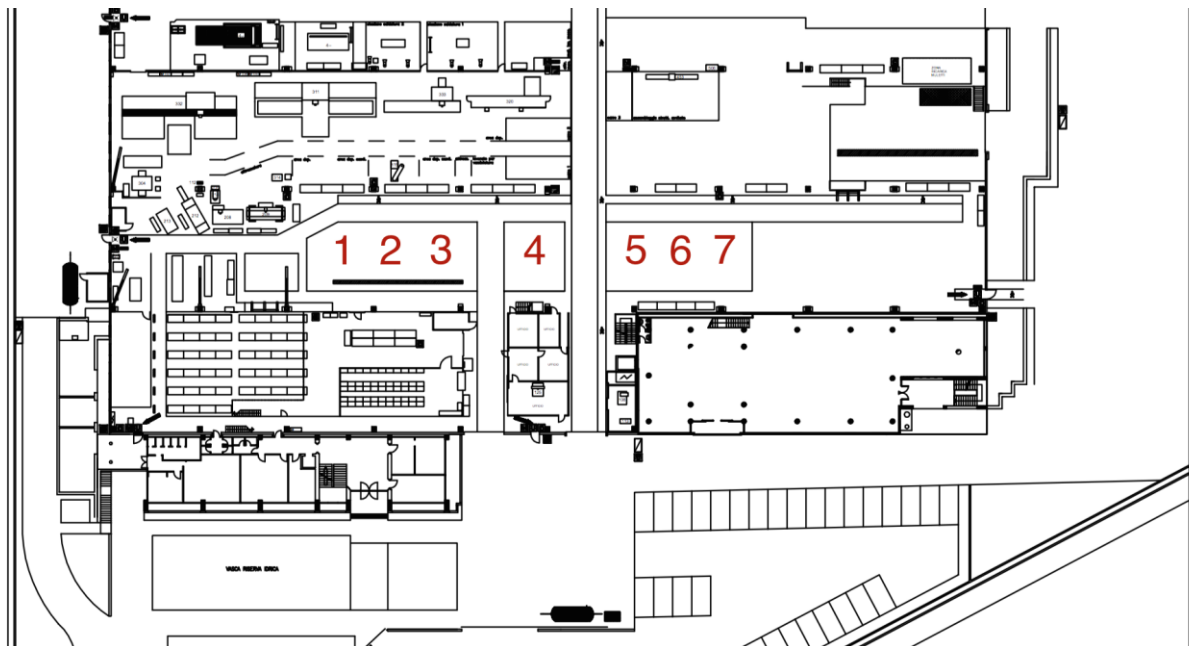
11: Individuazione delle stazioni di assemblaggio sul layout dello stabilimento
